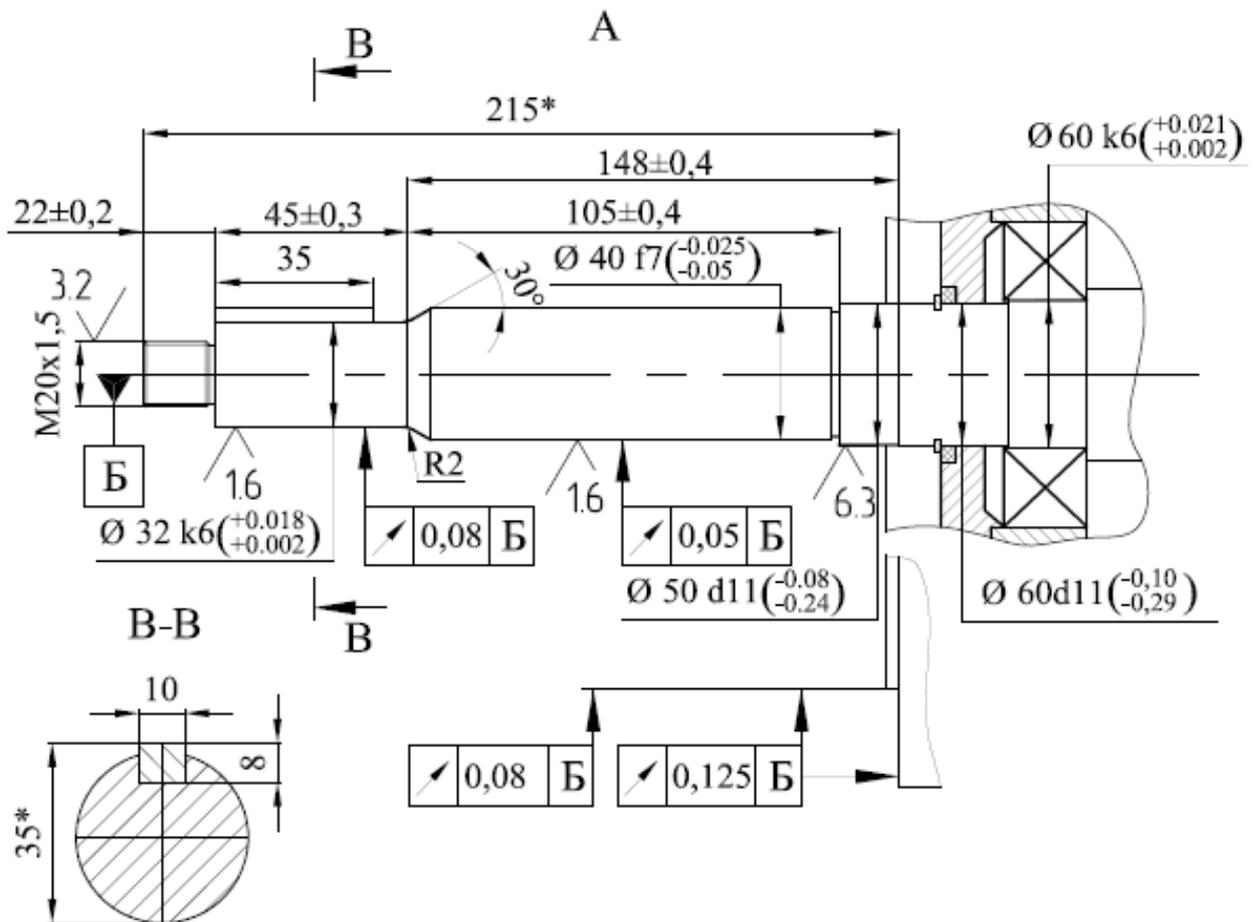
Свободный конец вала двигателя 6AMU180M2ЖУ2
